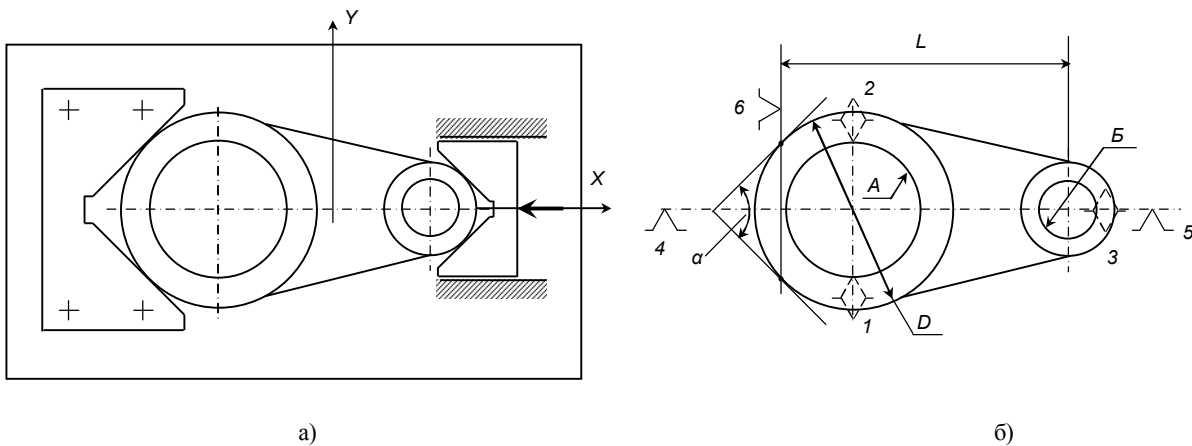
Конструктивна схема верстатного пристрою за варіантом 1 з установленою вихідною заготовкою (а) і відповідною схемою базування (б)
